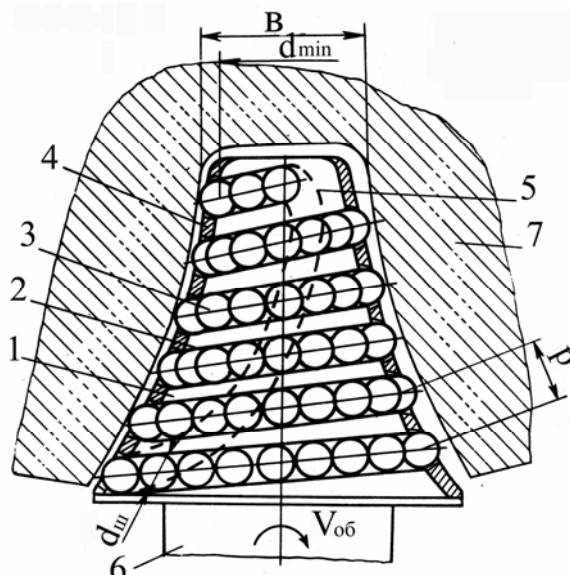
Устройство для обкатывания шариками зубчатых колес, винтов, реек
